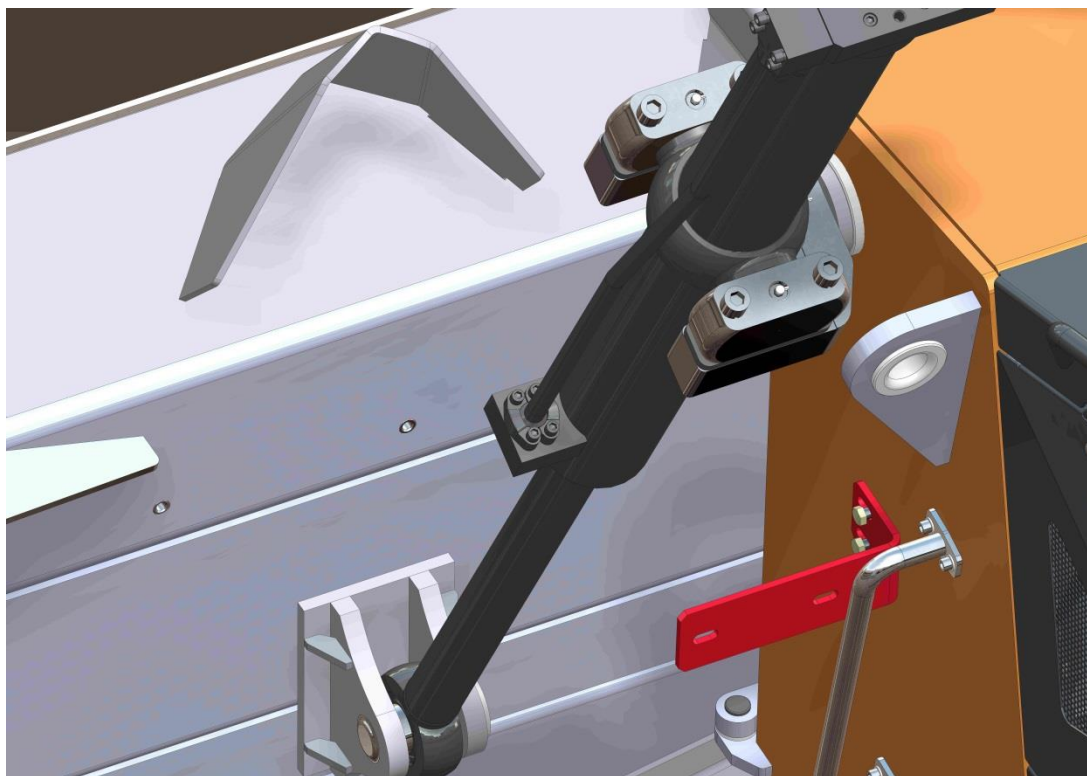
Монтаж гидроцилиндров подъема/заглубления отвала.
